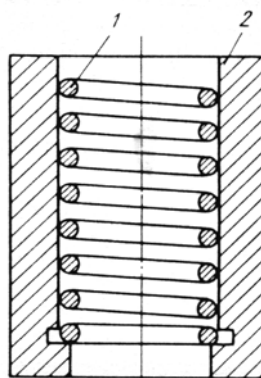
Пристрої для гартування пружин стиснення: 1- пружина; 2 - облямовування
